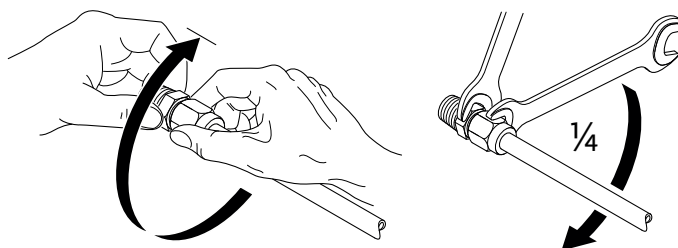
Ruotare ulteriormente il raccordo a compressione di 1/4 di giro
